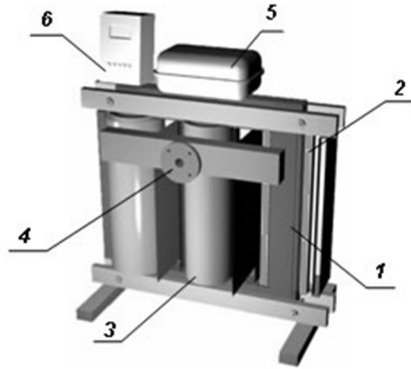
Общий вид индуктивно-кондуктивного нагревателя
